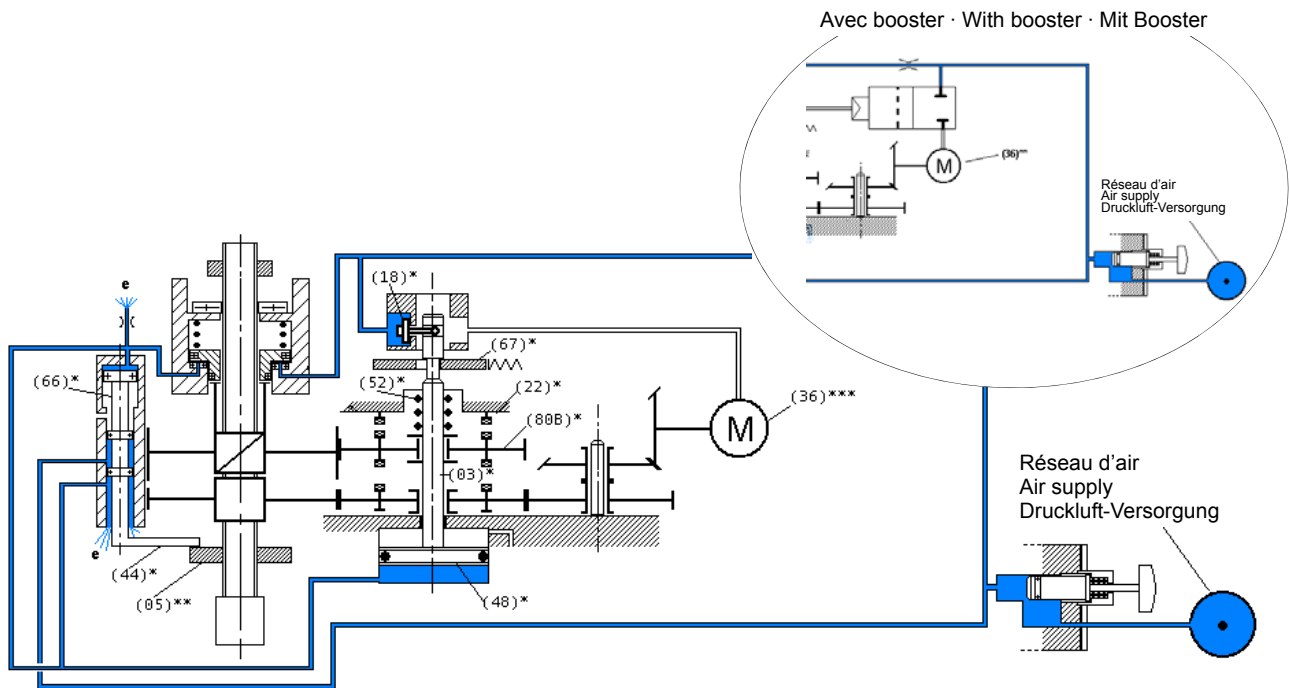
Fin de course arrière - Arrêt moteur • Backward limit switch position - Motor switch off •
